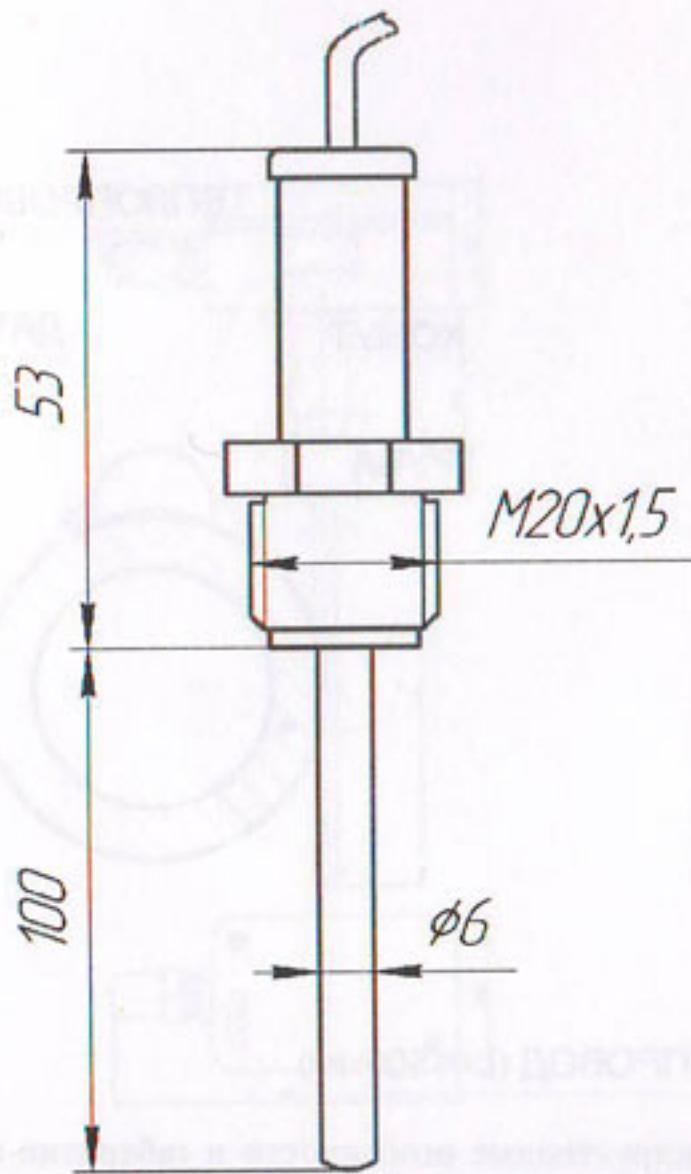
Конструктивные особенности и габаритно-присоединительные размеры датчика СТв-04
